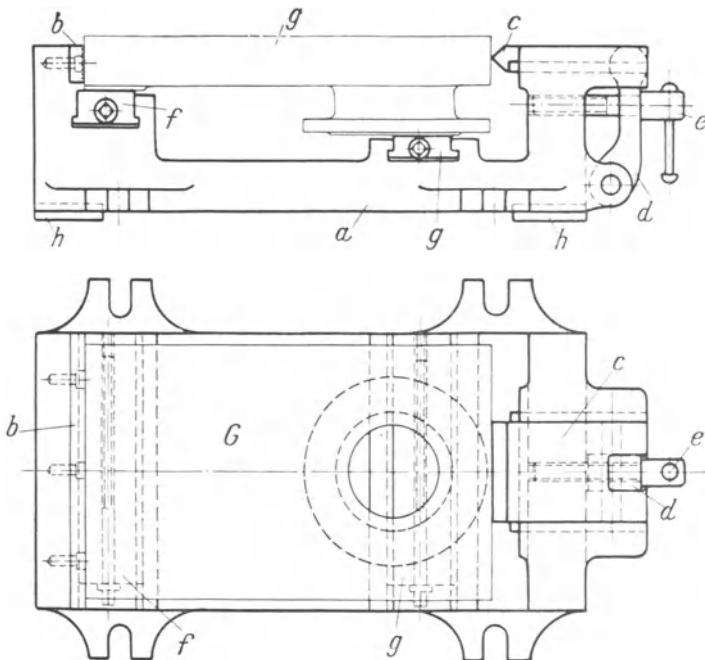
Hobelvorrichtung für Anschlußplatten.
